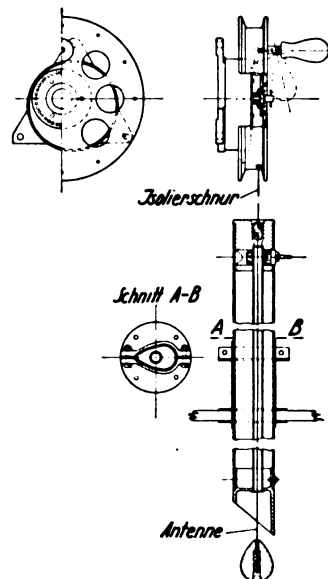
Schleppantennen-Anlage für Flugzeuge.
